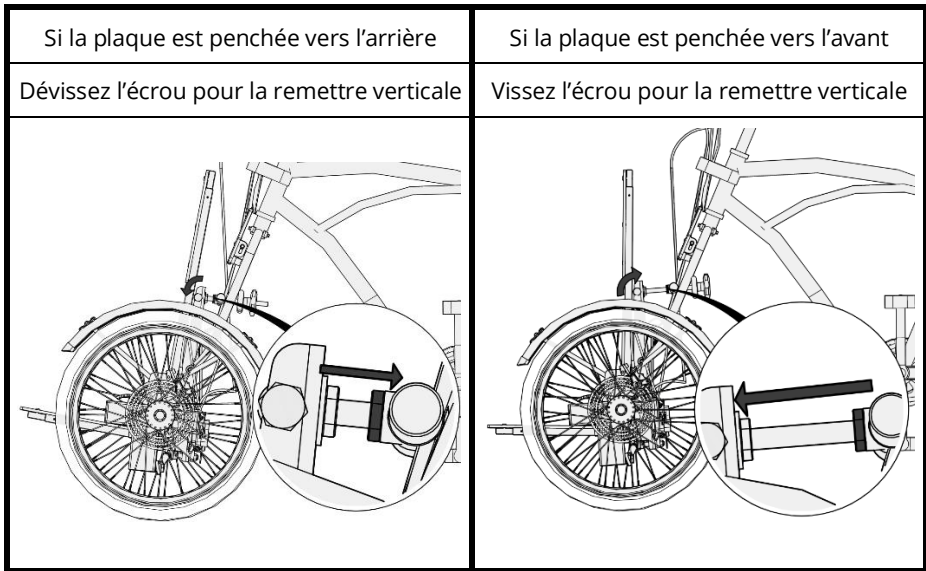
Réglage de l'inclinaison de la plaque arrière
